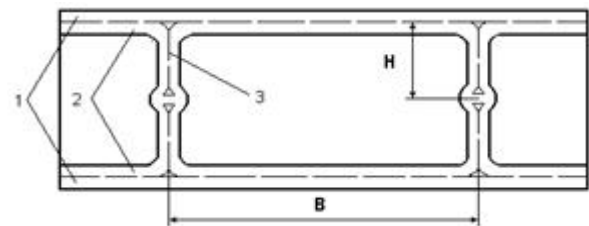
Схема многослойной ячеистой конструкции: 1 - обшивка; 2 - наполнитель; 3 - ребро жесткости. В и Н - ширина и высота ячейки.
